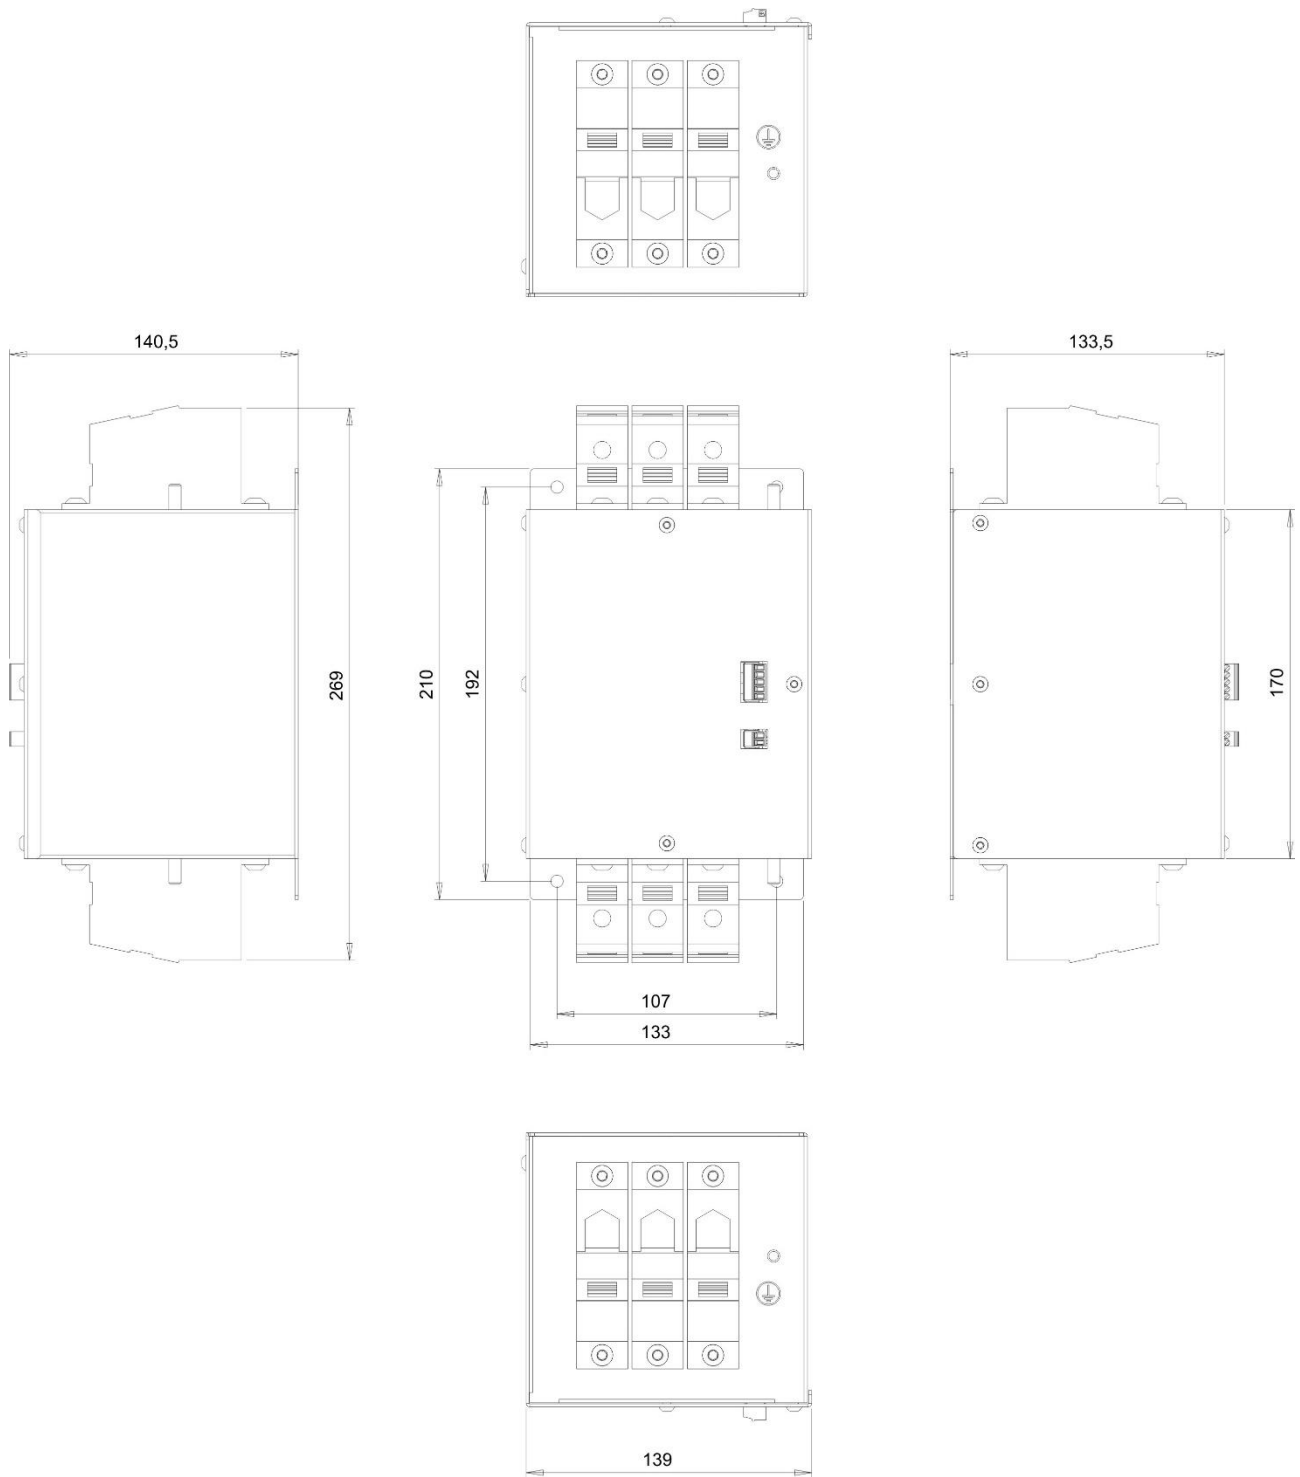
Dimensioni modulo sensori di corrente AFE Tless per OPDE S 70, 90, 110, 150, 175
